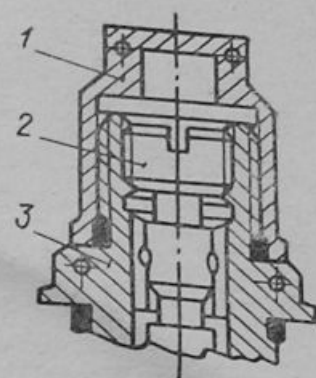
Регулировочный винт № 1 агрегата АТП в сборе:
